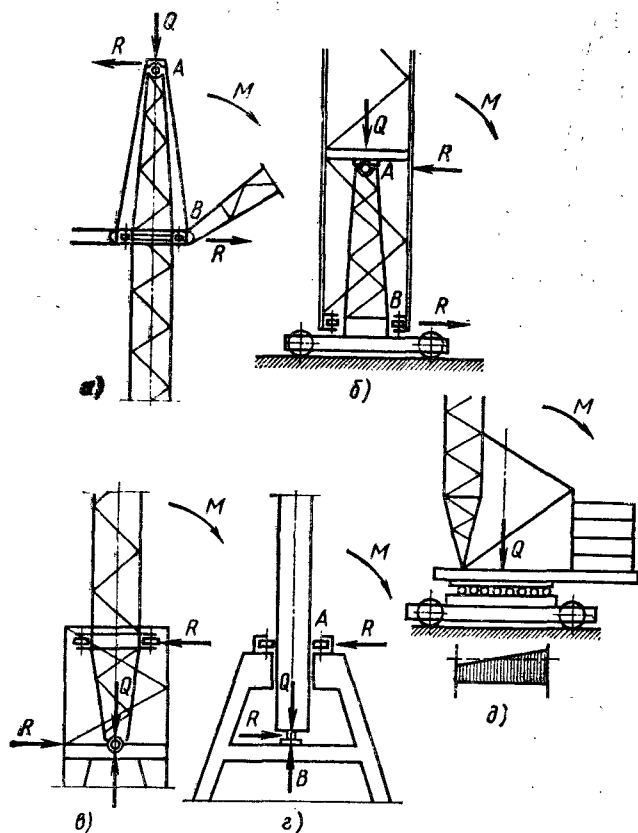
Схемы опорно-поворотных устройств строительных башенных кранов: а — кран с неподвижной башней и вращающейся стрелой; б — кран с поворотной башней, опирающейся на неподвижную колонну; в, г — краны, у которых башня является поворотной колонной; д — кран с поворотной платформой
